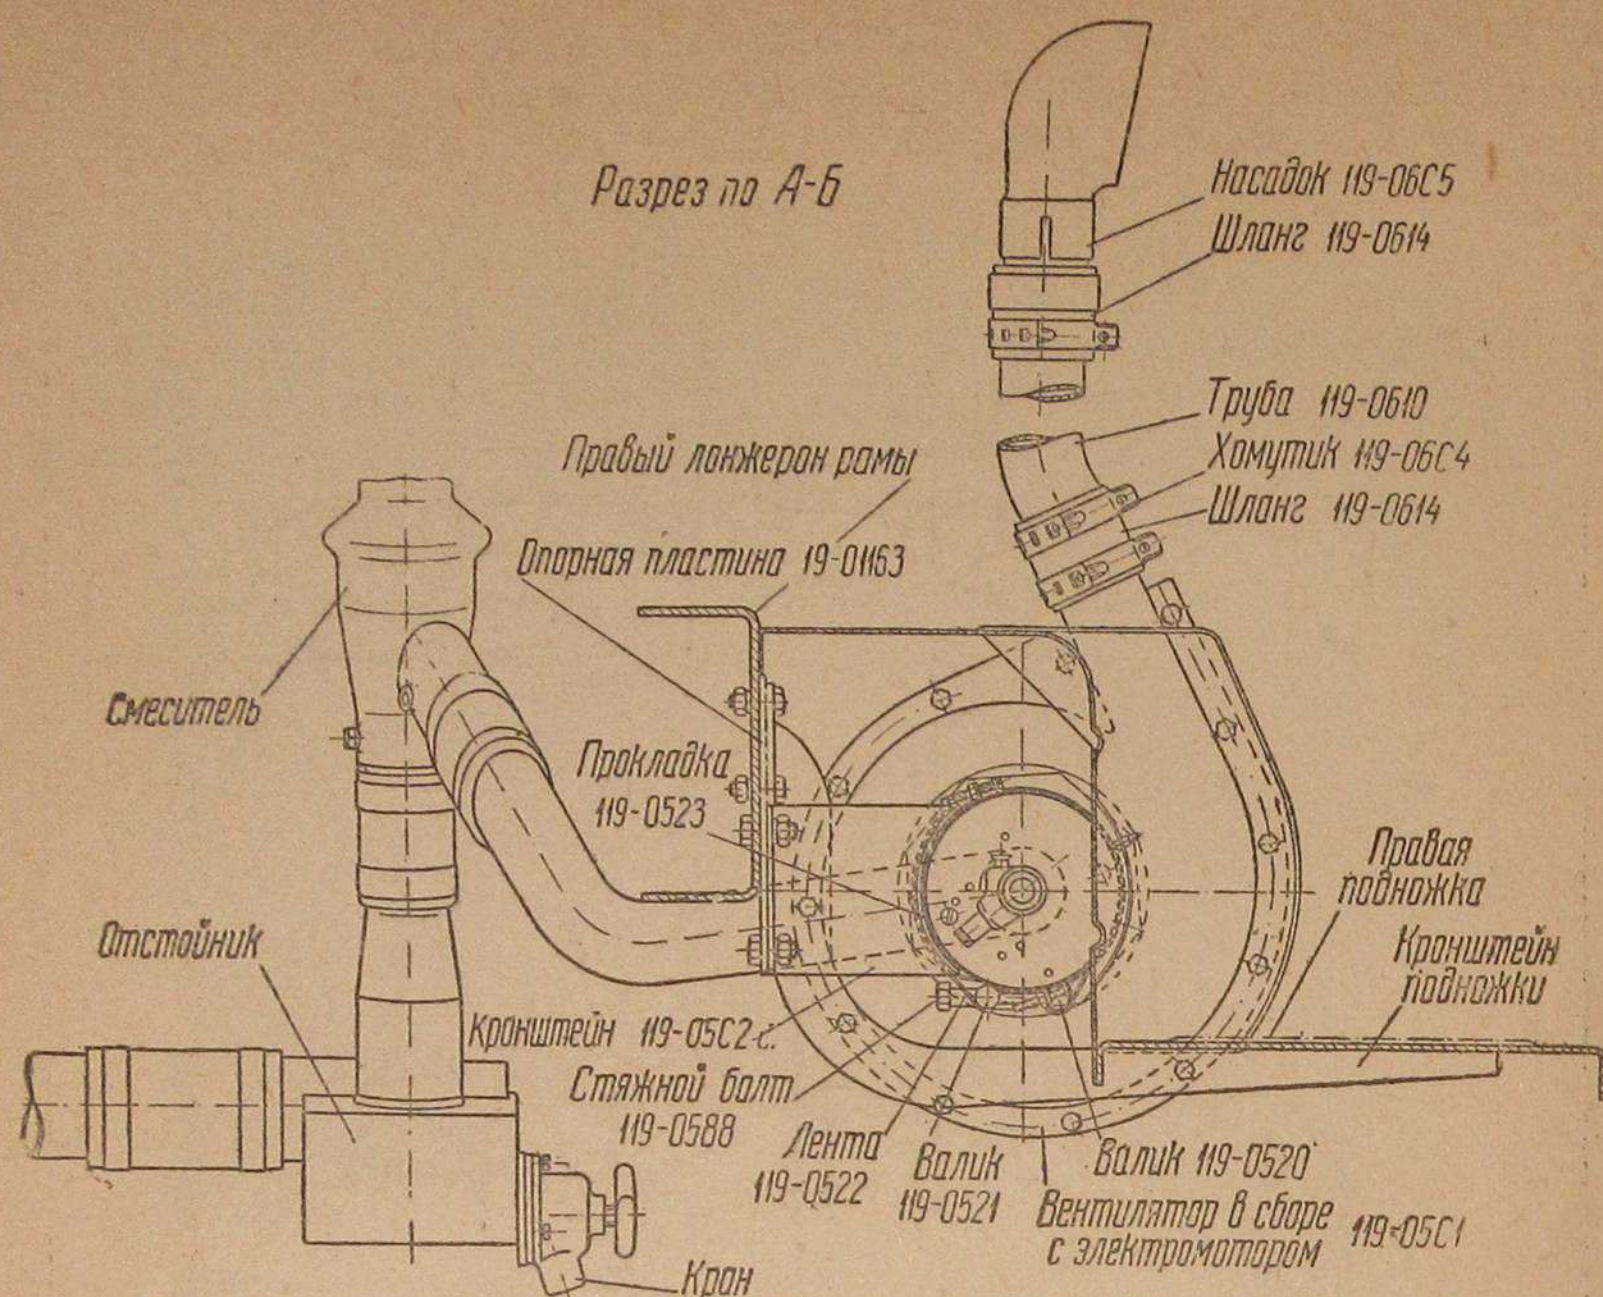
а. Установка на автомобиле раздувочного вентилятора и соединение его со смесителем
